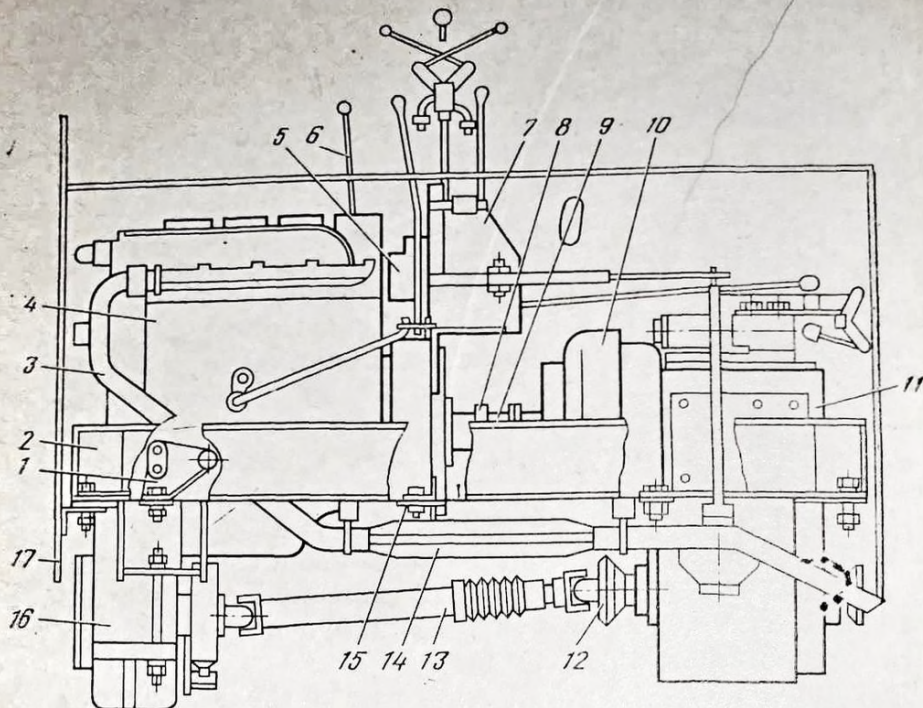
Установка двигателя и агрегатов катка ДУ-49А на подмоторной раме
